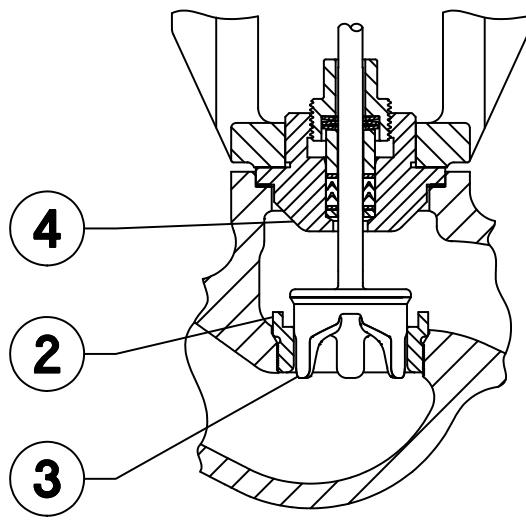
Разгруженный трим клапана GX Fisher (стандартно для размеров Ду 80 и 100 [номинальный размер трубы 3 и 4])
